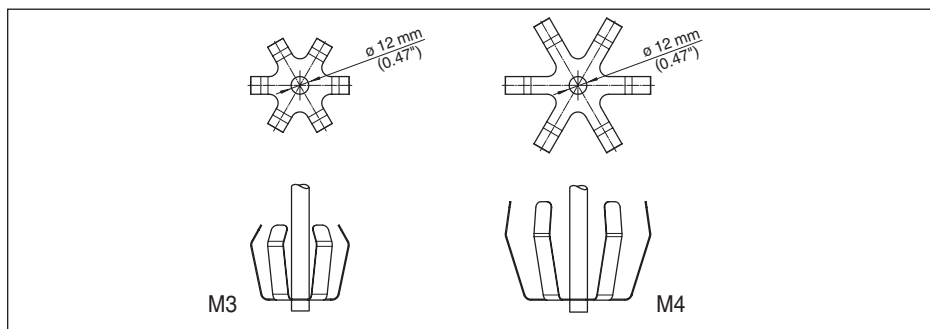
Центрирующие звездочки из металла для стержневых исполнений с \varnothing 12 мм (0.47 in)
